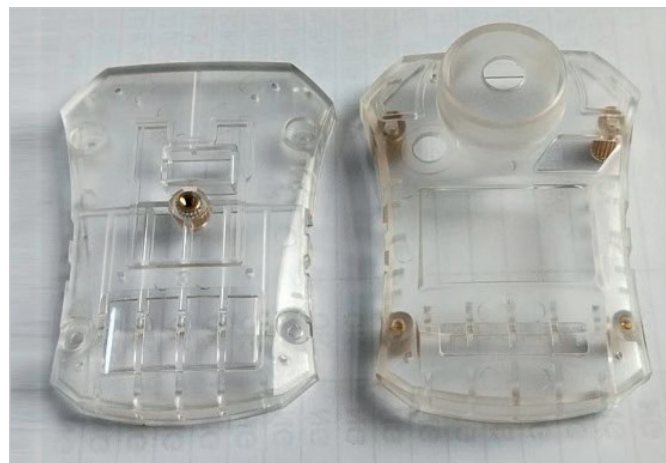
Одна из форм корпуса с закладными металлическими винтами
